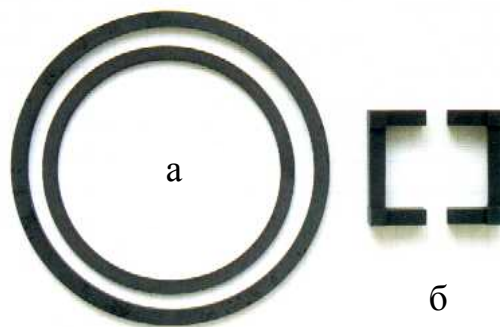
Осердя з ферокераміки для електромагнетних відчутників, де: а – осердя для фрезерних верстатів, б – осердя для токарного інструмента
